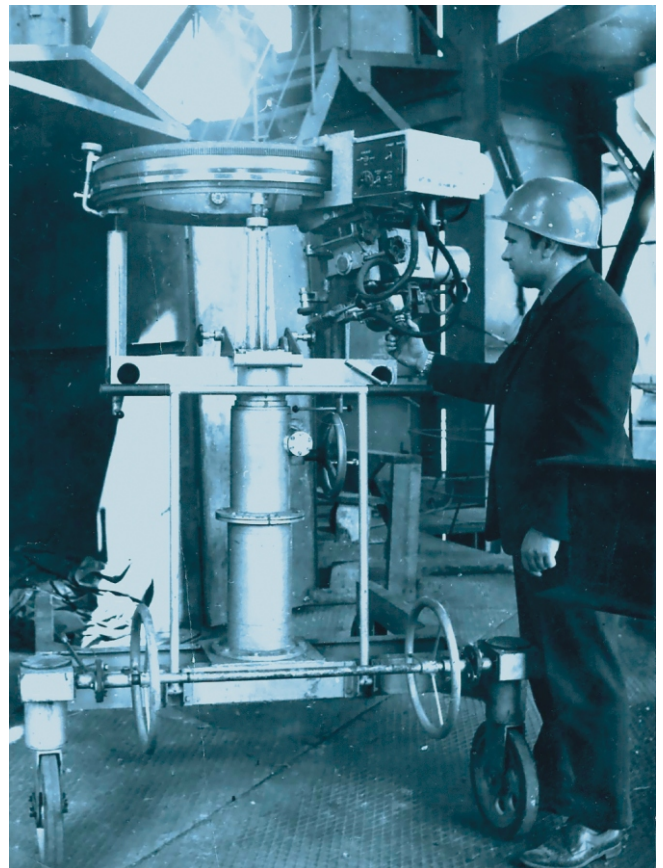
Сварочный аппарат А-1311, расположенный на технологической транспортной тележке
